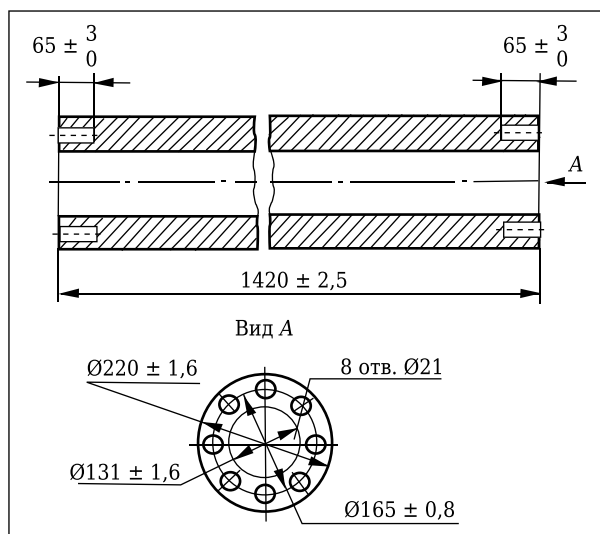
Кварцевая оболочка ролика для транспортировки стальной ленты в печах обжига динамной стали
